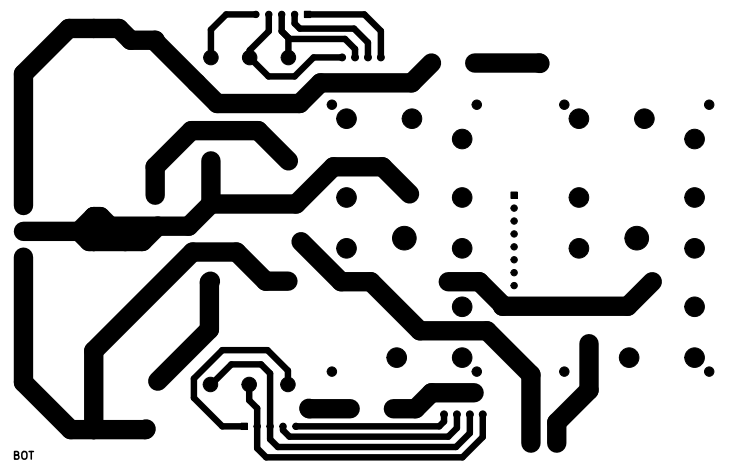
Footprint* da PCB dos módulos + sensores (*bottom layer*).
